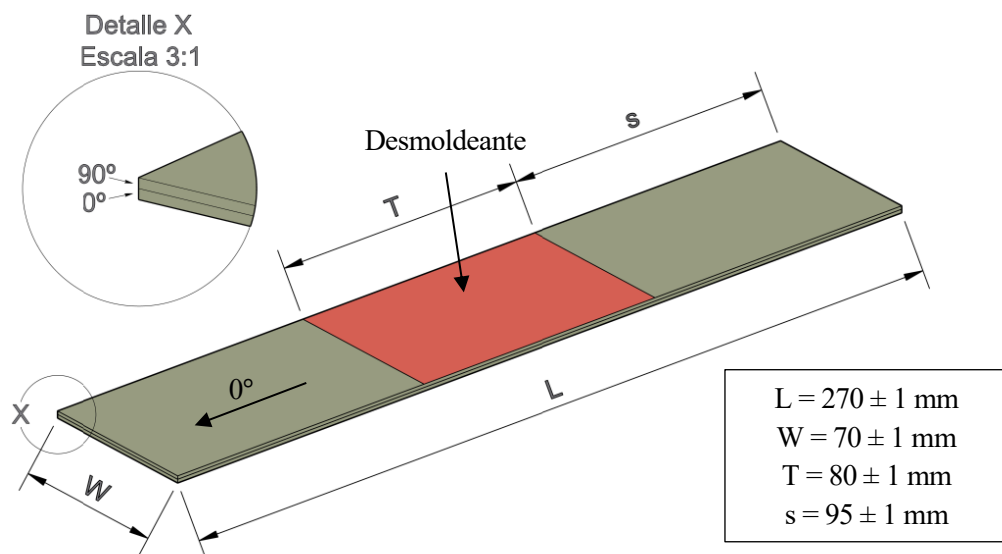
Apilado de la lámina desmoldeante central del panel 2
